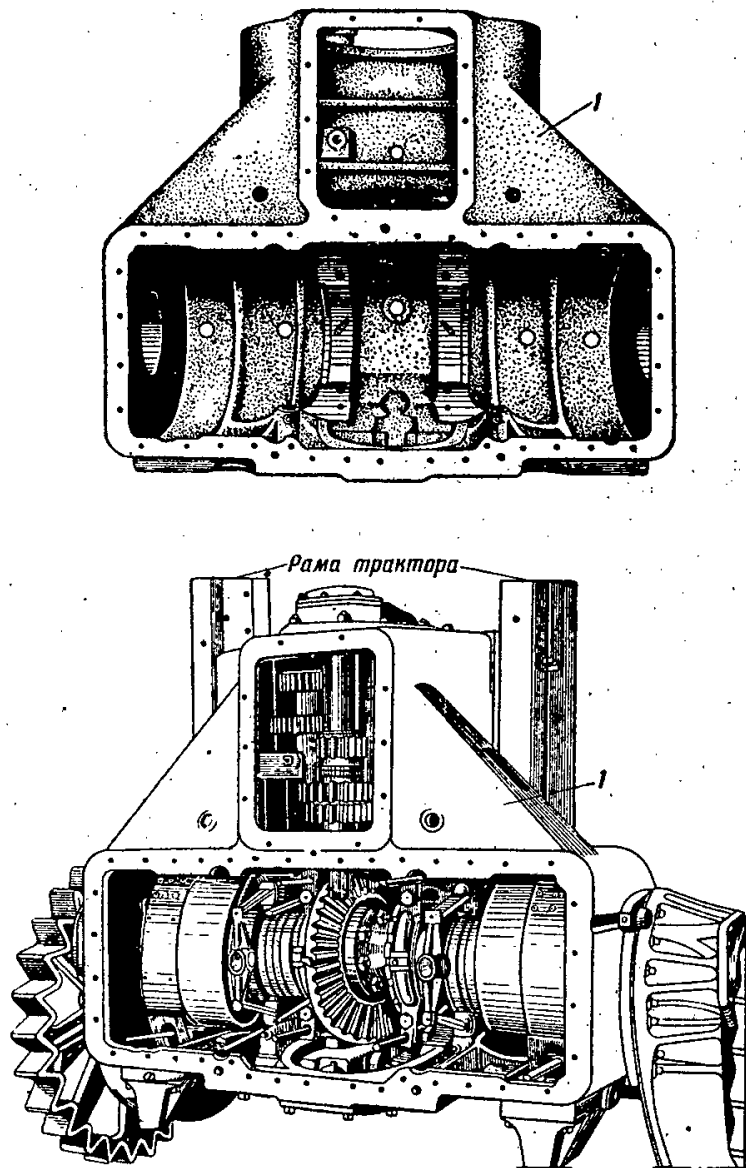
Общий вид корпуса коробки перемены передач тракторов С-60 и С-65
